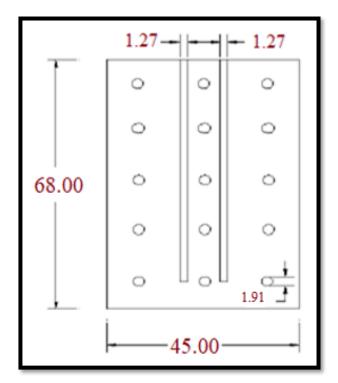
Vista en planta de la plancha metálica. Fuente: Propia
